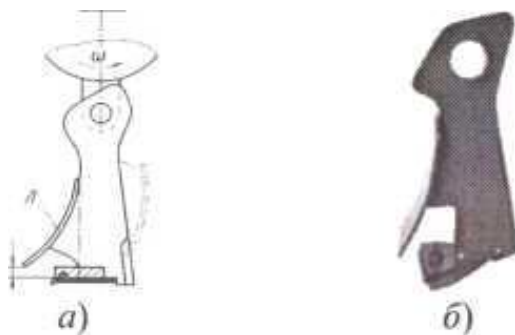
Шарнирный нож измельчителя ИСН-3,5: а - схема ножа; б - фото ножа.
